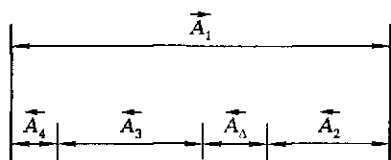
Схема размерной цепи подшипникового узла с числом звеньев $m = 5$
